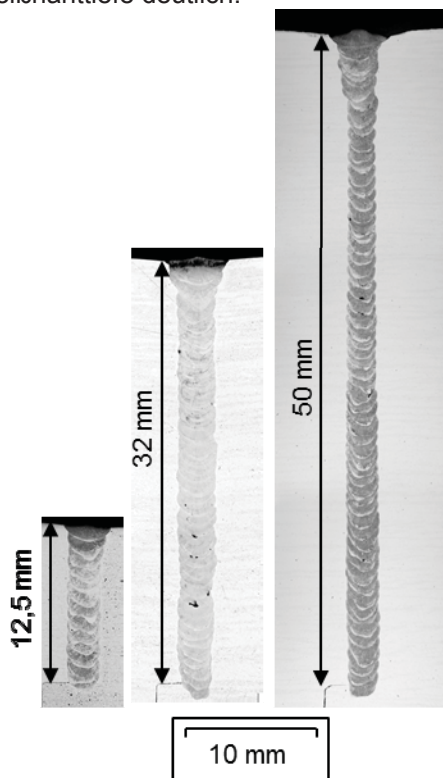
Querschliff einer  $12,5\ \text{mm}$  tiefen Schweißnaht
